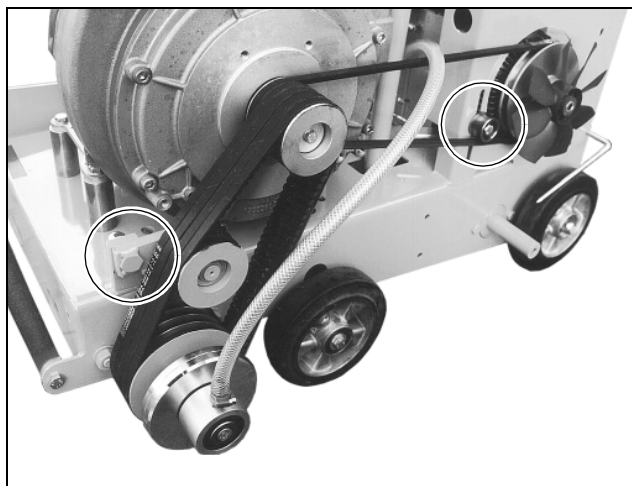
Устройство регулировки натяжения клиновых ремней
